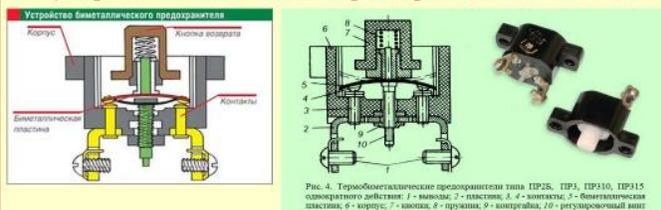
Термобиметаллические предохранители типа ПР2Б, ПР3, ПР310, ПР315 однократного действия: 1 - вывозка; 2 - пластина; 3, 4 - контакты; 5 - биметаллическая пластина; 6 - корпус; 7 - катушка; 8 - пружина; 9 - изопробой; 10 - регулировочный винт
